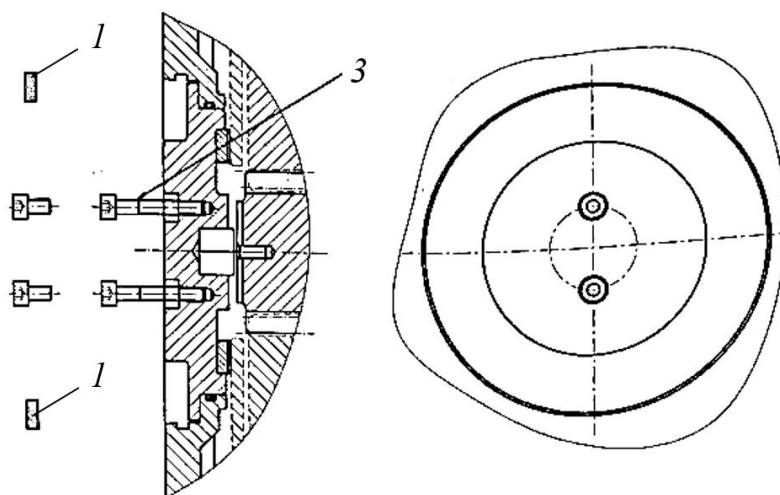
Процесс подготовки к снятию крышки редуктора
